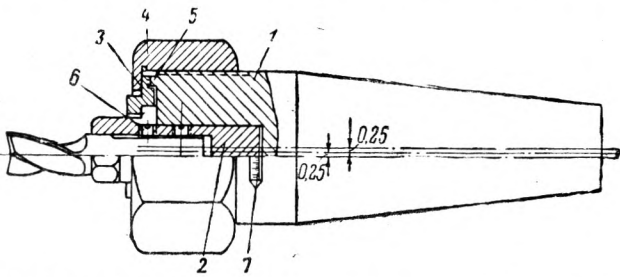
Общий вид патрона для регулирования ширины паза при фрезеровании концевыми фрезерами с маятниковой подачей.
